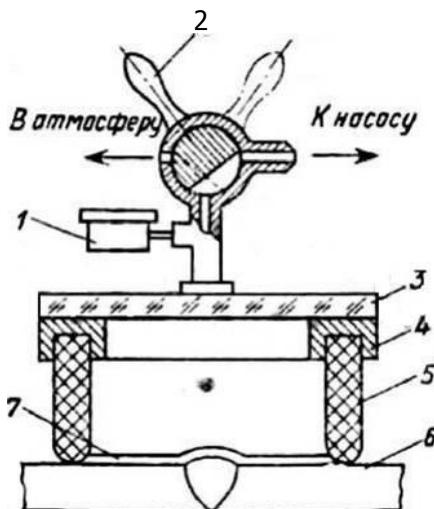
Схема контроля герметичности с помощью вакуумной камеры: 1 - вакуумметр, 2 - трехходовой кран (в двух положениях), 3 - оргстекло, 4 - металлическая рамка, 5 - губчатая резина-уплотнитель, 6 - контролируемое сварное соединение, 7 - пленка пенообразующего вещества
